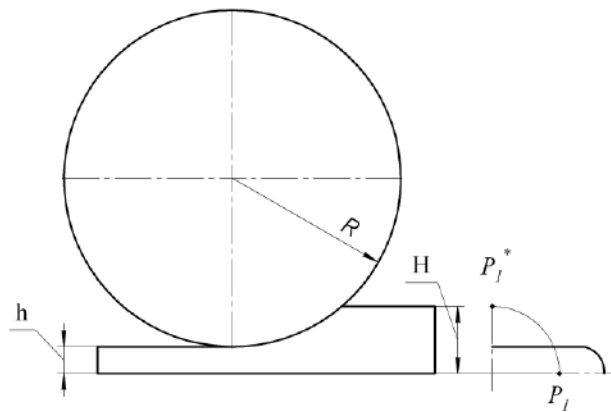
Схематичне представлення процесу вальцювання заготовок [85]
